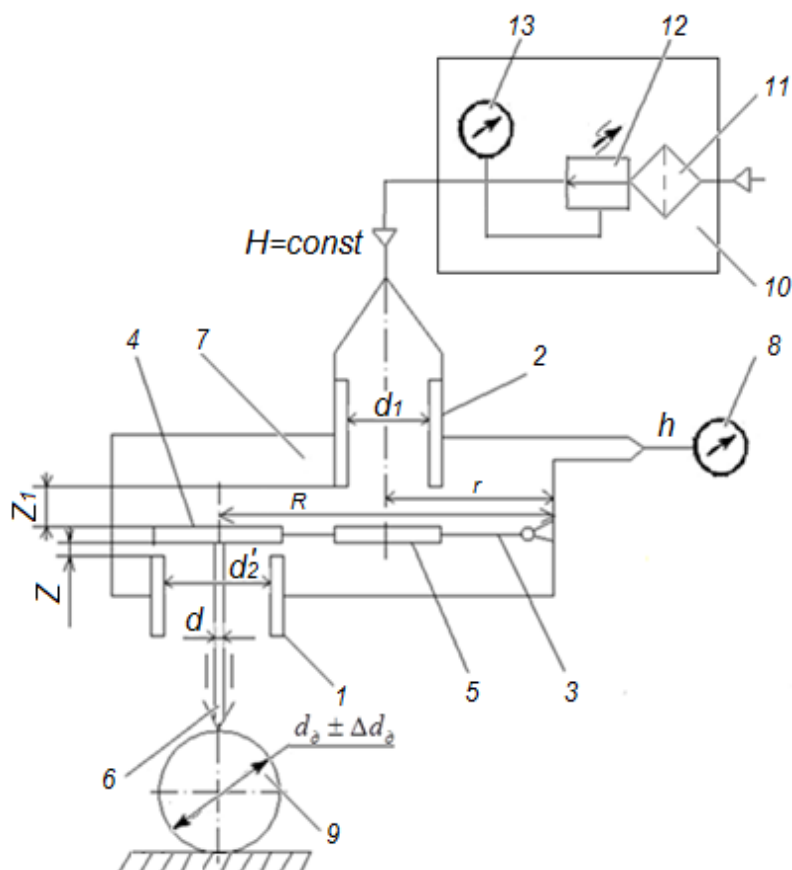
Принципиальная схема рычажного пневматического преобразователя с двумя регулируемым соплами:
